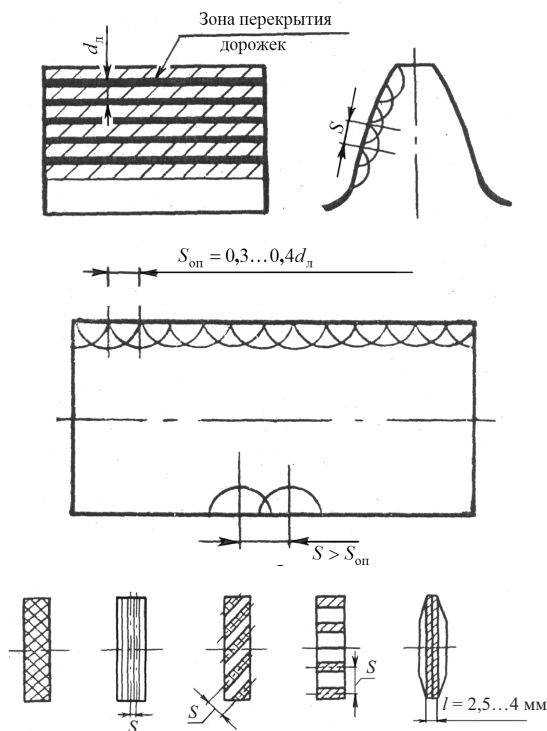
Схемы расположения зон лазерной обработки поверхности образцов для испытаний
